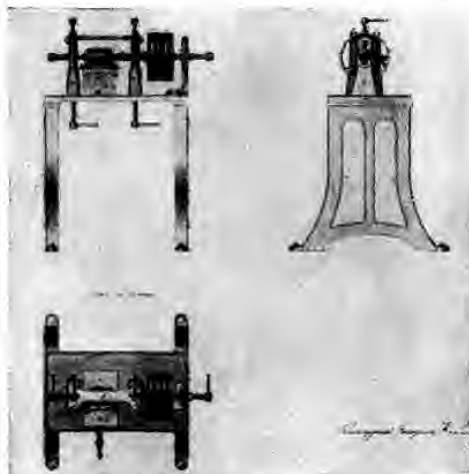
Горизонтально-фрезерный станок Ижевского завода. 1862 г. Заводской чертеж.
